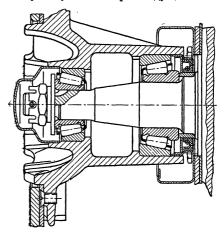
Опоры переднего колеса грузового автомобиля на конических роликоподшипниках
